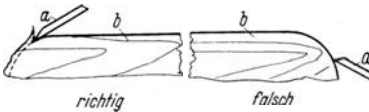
Ansetzen des Stemmisens. *a* = Werkzeug; *b* = Werkstück.
